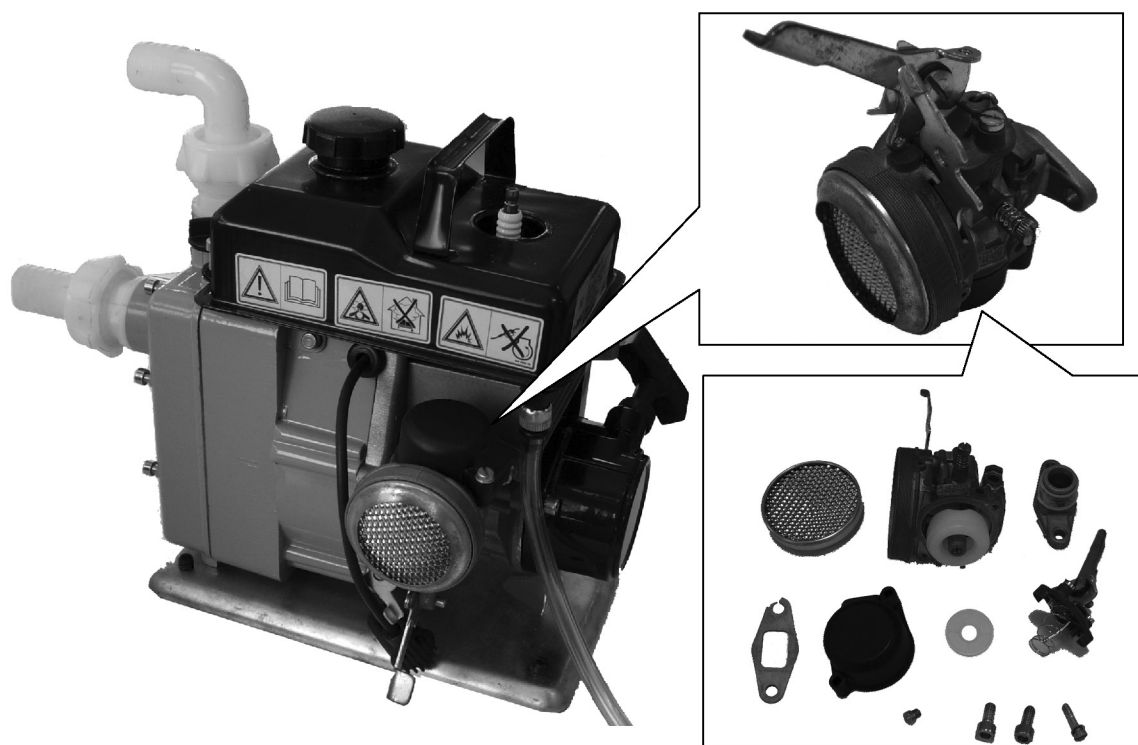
Conjunto motobomba de extracción de agua, impulsada por un pequeño motor de combustión interna, con subconjunto de carburador y despiece del mismo
